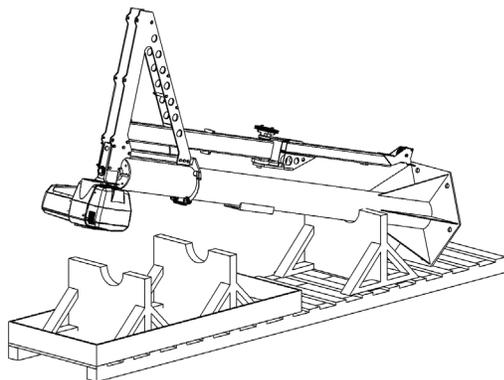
D. Rimozione del dispositivo Easy Arm® dall'imballaggio.
